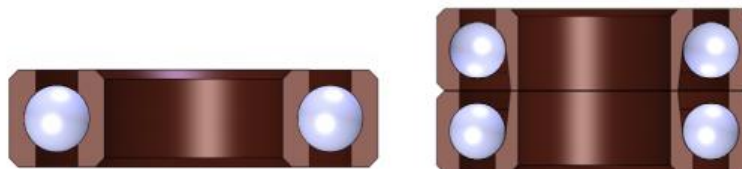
Однорядный (а) и двухрядный (б) подшипник качения
